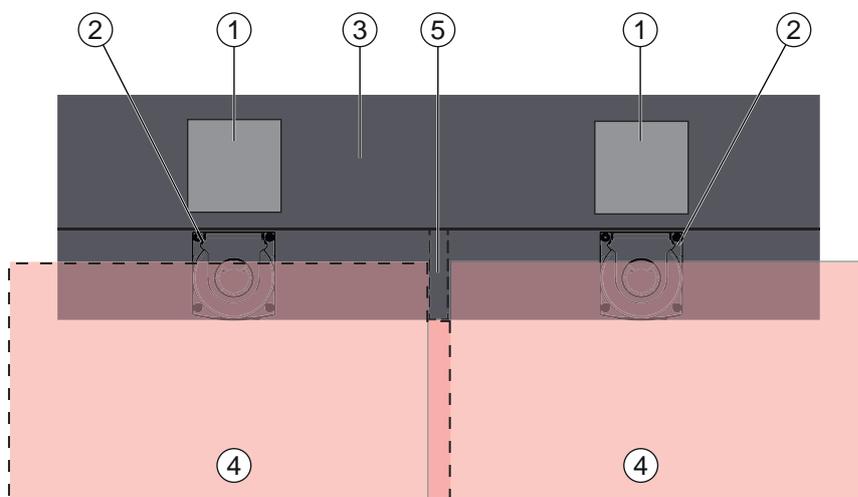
Hintertreterschutz durch Einsenkung in die Maschinenkontur
